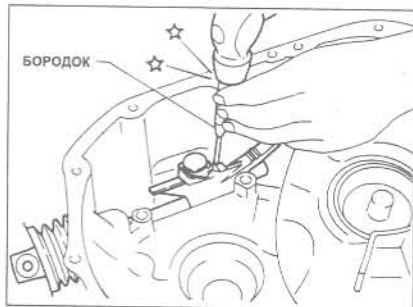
Установка крепежного штифта рычага (Глава 14)
